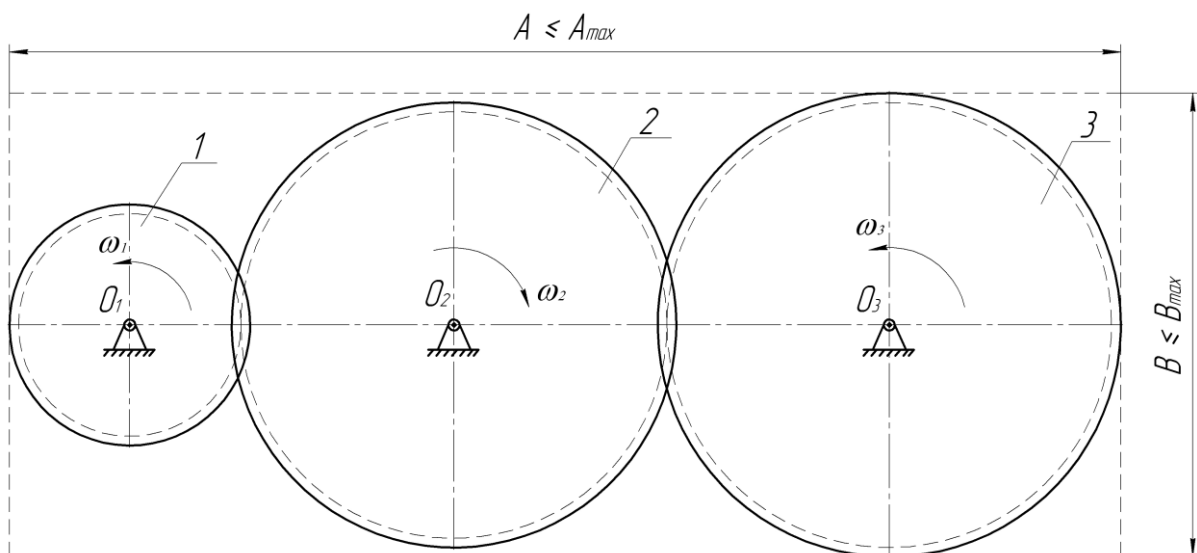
Кінематична схема рядового зубчатого механізму
